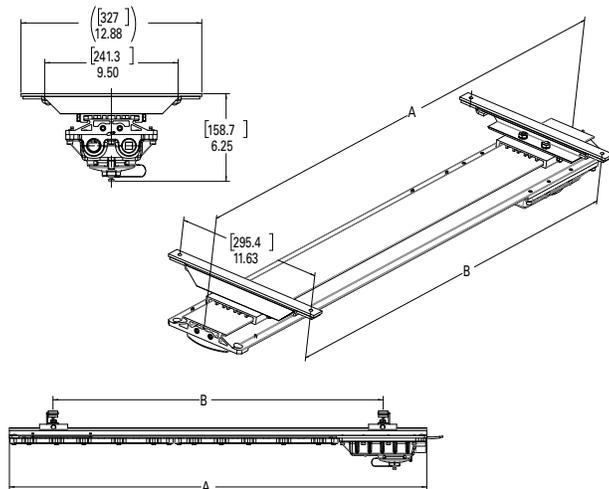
Installation du support MagnaPro ou Surface de la trousse MP1054MTK
